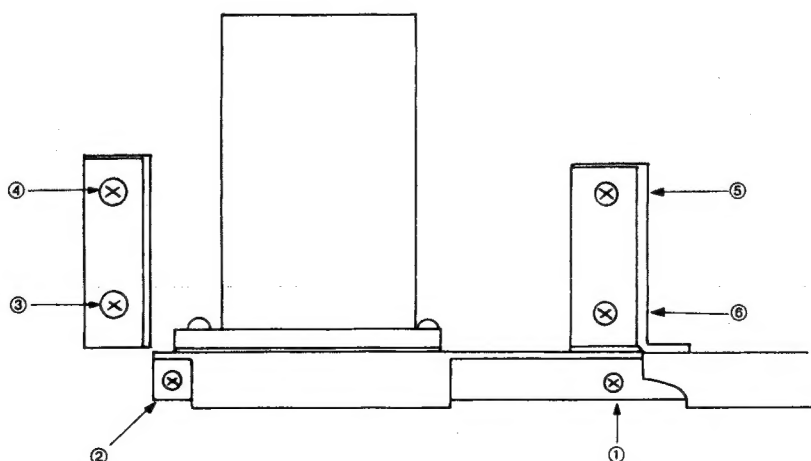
Vue arrière de l'unité de mécanisme de rotation (côté droit)
